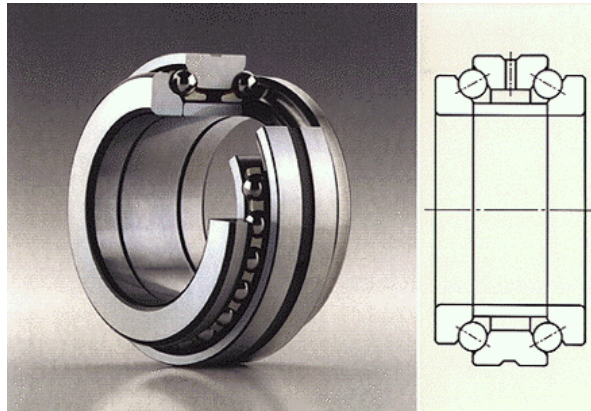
Rodamiento axial de bolas de contacto angular de doble efecto.
